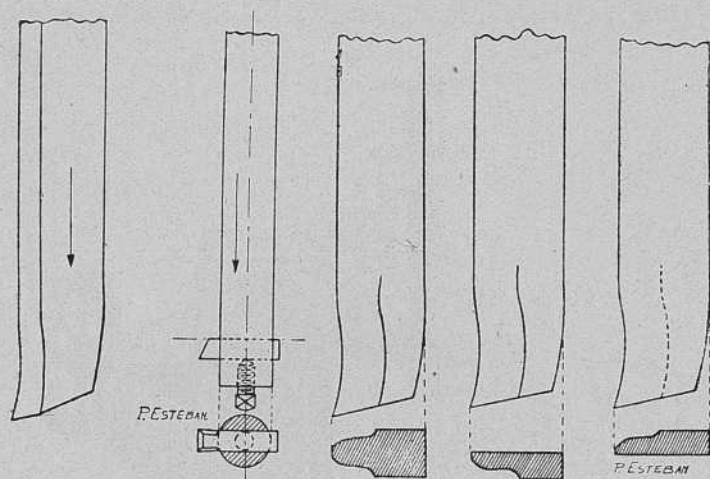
y 81. — Herramientas para abrir ranuras de chaveta. Fig. 582-84. — Herramientas para construir engranajes en la mortajadora.
